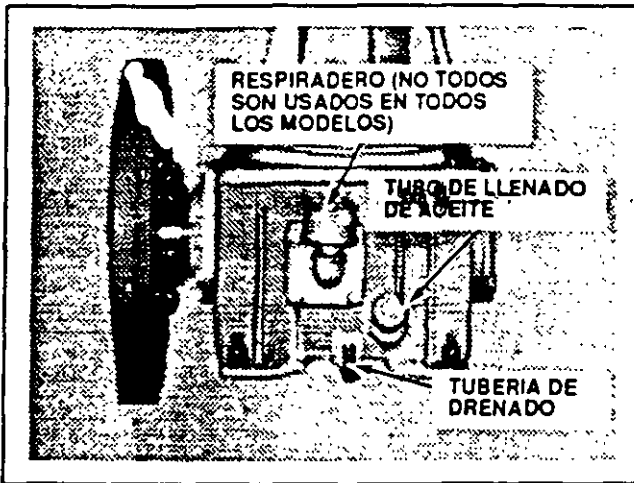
DRENADO Y LLENADO DE ACEIRE DE LA UNIDAD DE ENGRANES DEL VENTILADOR DE RADIADORES. E-32381-S
